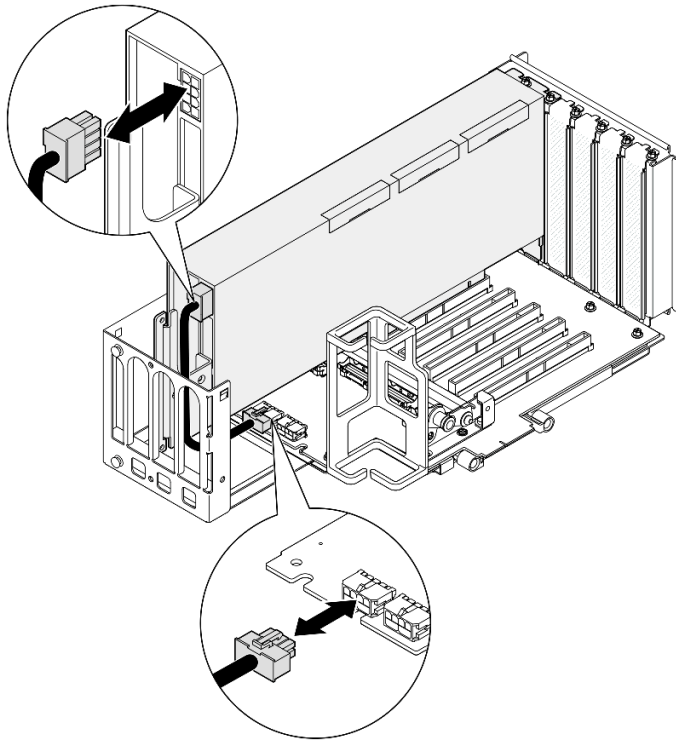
Desconectando o cabo de alimentação do adaptador de GPU
